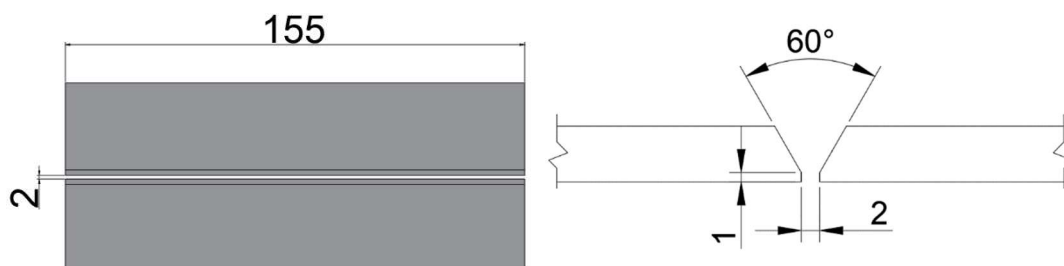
Ilustração esquemática da junta de soldadura da amostra E.
